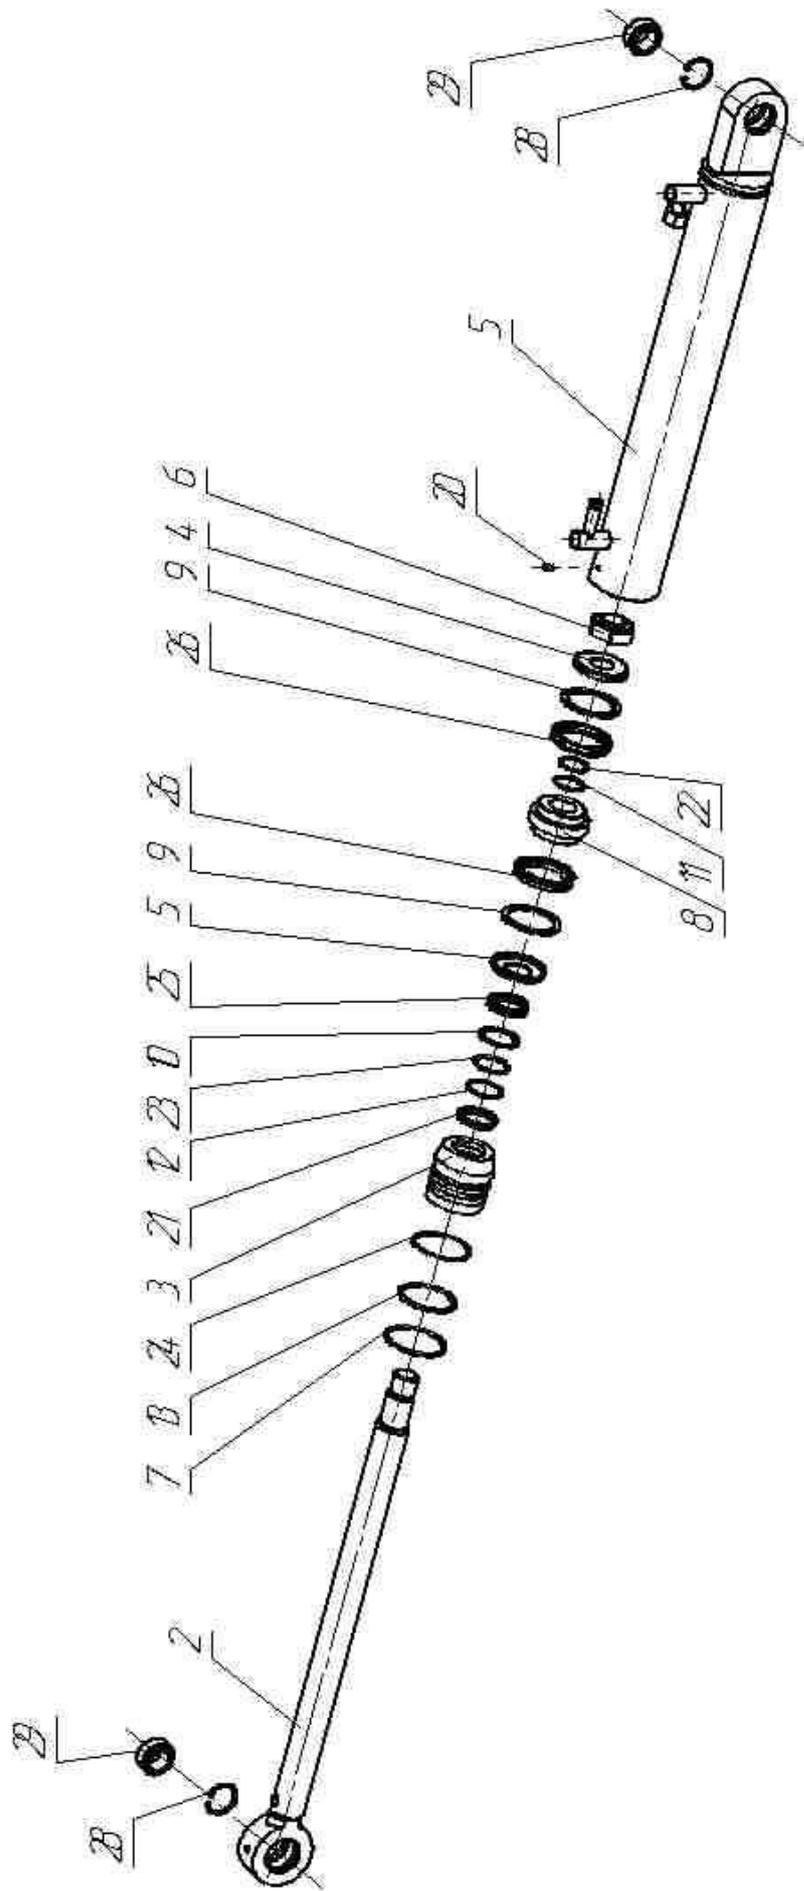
Гидроцилиндр поворота рукоятки КОРС-1100.03.100
